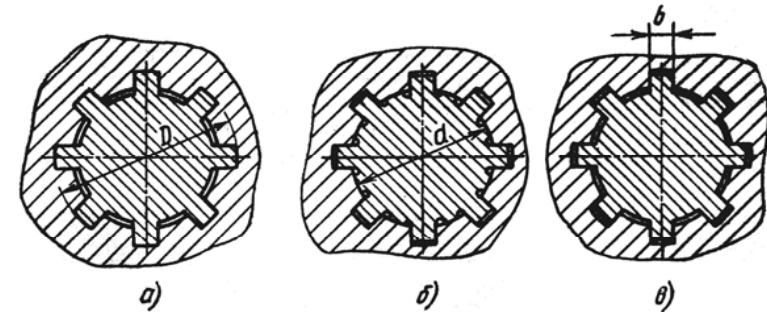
Шлицевые соединения с прямобочным профилем
